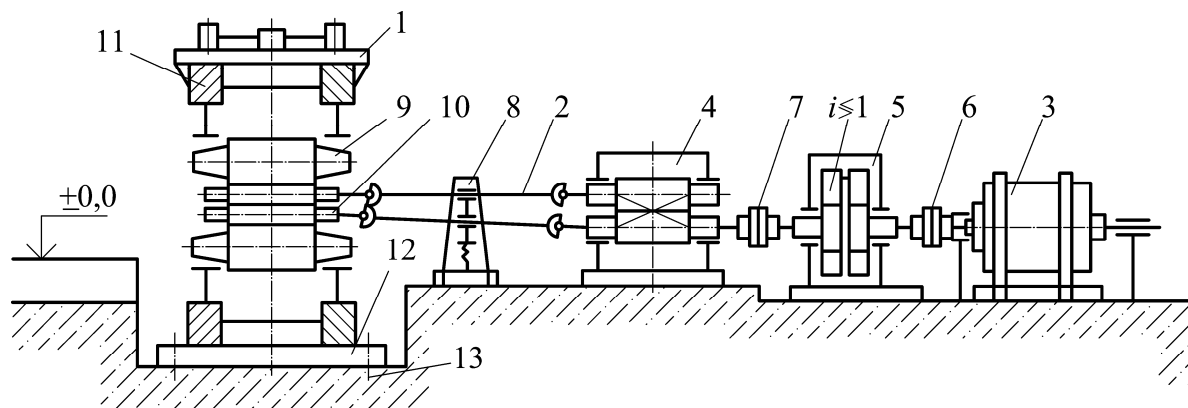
Схема главной линии четырехвалковой рабочей клетки: 1 – рабочая клетка; 2 – универсальные шпиндели; 3 – электродвигатель (главный привод); 4 – шестеренная клетка; 5 – редуктор; 6 – моторная муфта; 7 – коренная муфта; 8 – пружинное уравнивающее устройство шпинделей; 9 – опорные неприводные валки; 10 – рабочие приводные валки; 11 – станина; 12 – плитовина; 13 – анкерный болт
